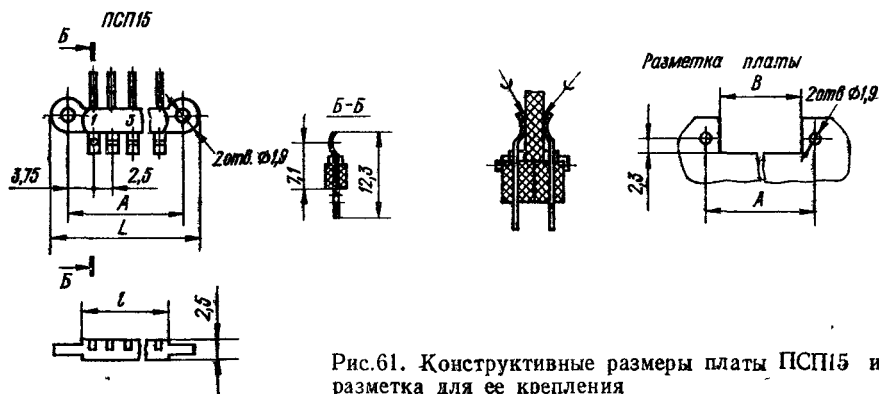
Конструктивные размеры платы ПСП15 и разметка для ее крепления
